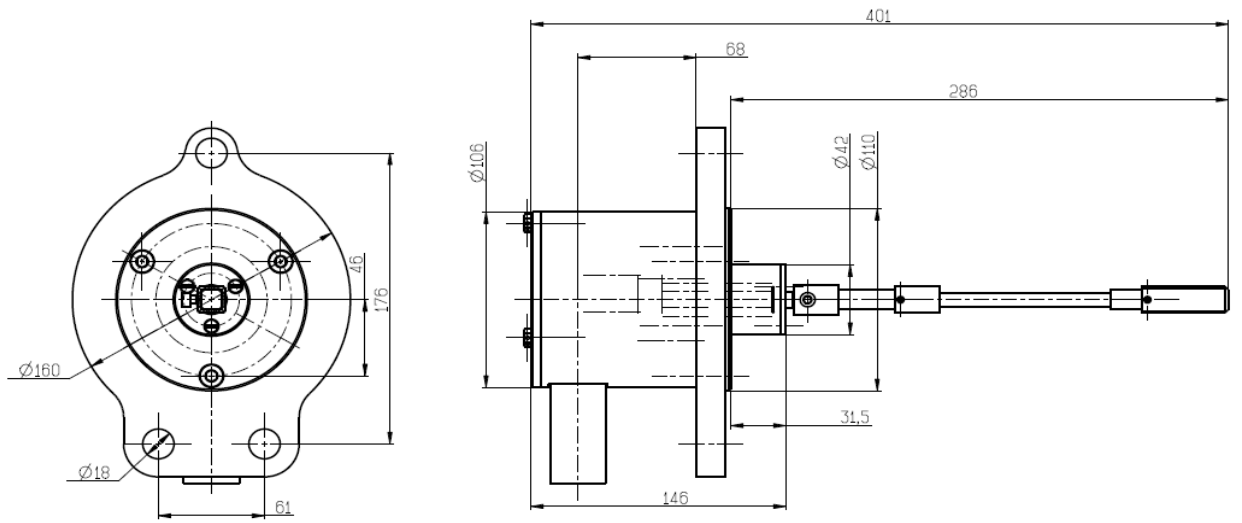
Рисунок 1. Конструкция, габаритные и присоединительные размеры датчика ДС-01 с фланцем для установки на крышку будки тепловозов ТГМ-4 и ТГМ-6.
